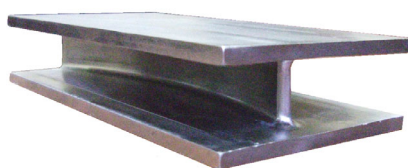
Технологическая схема получения заготовок для изготовления макетов полого колеса и полый широкохордной лопатки .
